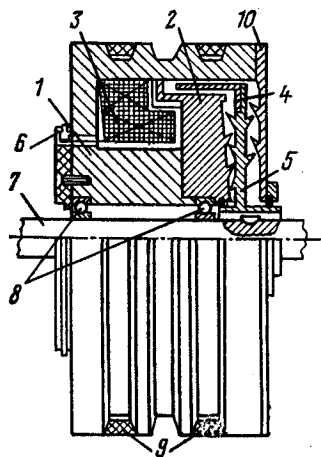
Конструкция малоинерционной порошковой муфты: 1 — корпус муфты; 2 — башмак; 3 — обмотка; 4 — обод ротора; 5 — втулка ротора; 6 — контактные кольца; 7 — ведомый вал; 8 — подшипники; 9 — ремни; 10 — крышка
